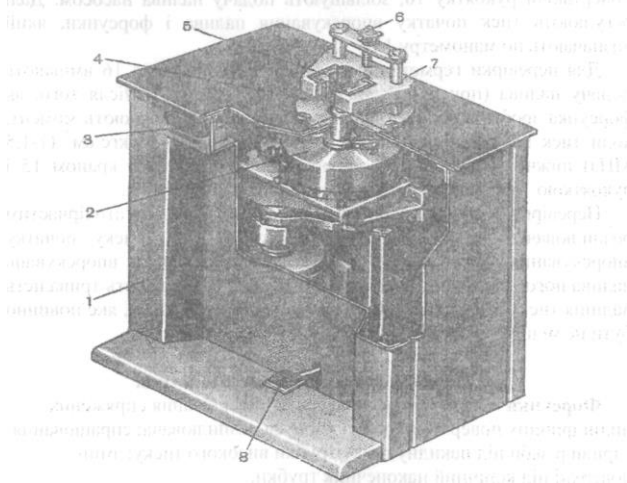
Стенд КИ-5227 для розбирання і складання форсунок: 1 – станина стенду; 2 – регулювальна муфта; 3 – реверсивний вмикач; 4 – опорна плита; 5 – установочна призма; 6 – маховичок; 7 – траверса; 8 – педаль; 9 – торцеві ключі.
